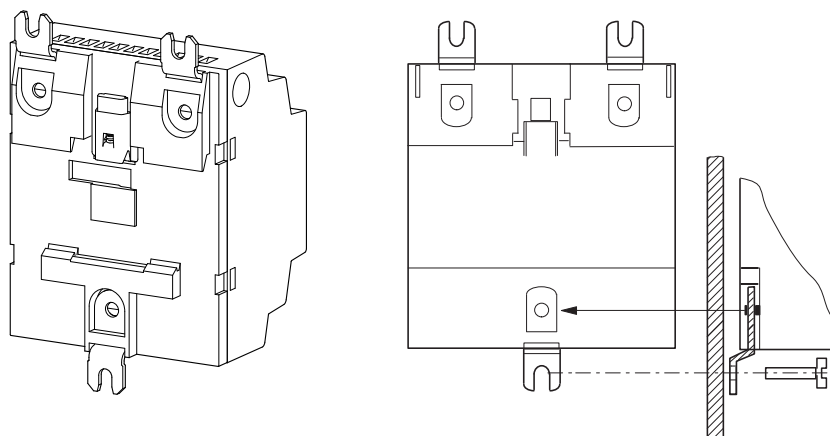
Exemple : fixation par vis d'un appareil 4PE
